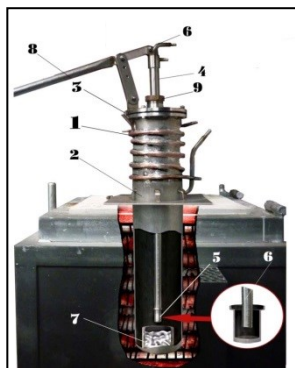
Технологический комплекс для формирования на поверхности полых деталей наноструктурированных покрытий: 1- труба для подачи охлаждающего агента; 2 - цилиндрический корпус; 3 - герметичная крышка; 4 - трубка для фиксации изделия; 5 – обрабатываемое изделие; 6 - трубка для подачи охлаждающего агента; 7 - ванна с жидкометаллическим носителем; 8 – рычаг; 9 – зажимная гайка
